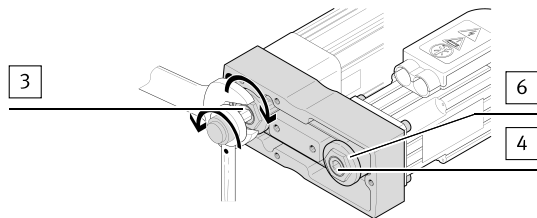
Затяжка до упора шкивов зубчатого ремня
